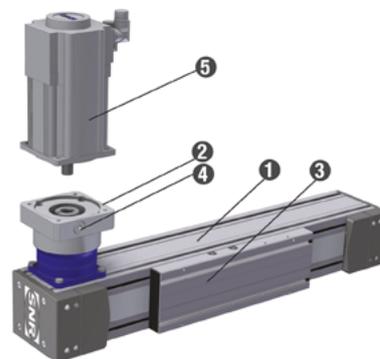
Motormontage an Linearachsen Planetengetriebe
